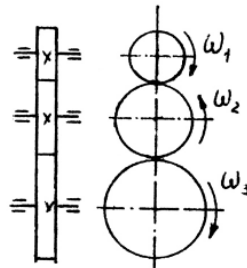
Рядовий зубчастий механізм з кінчними колесами
